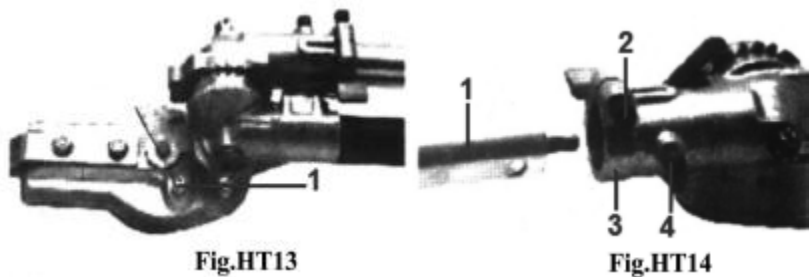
1. Raccord de graissage du carter d'engrenage
